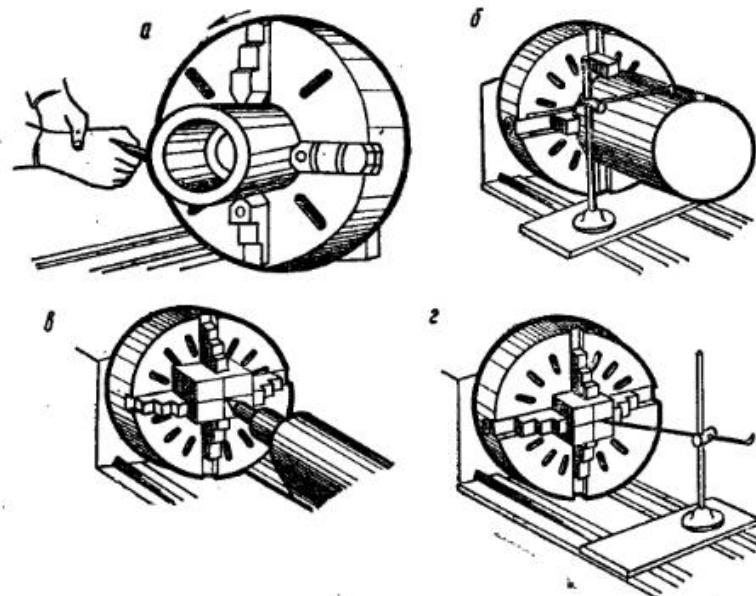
Выверка заготовок в 4-кулачковом патроне:
